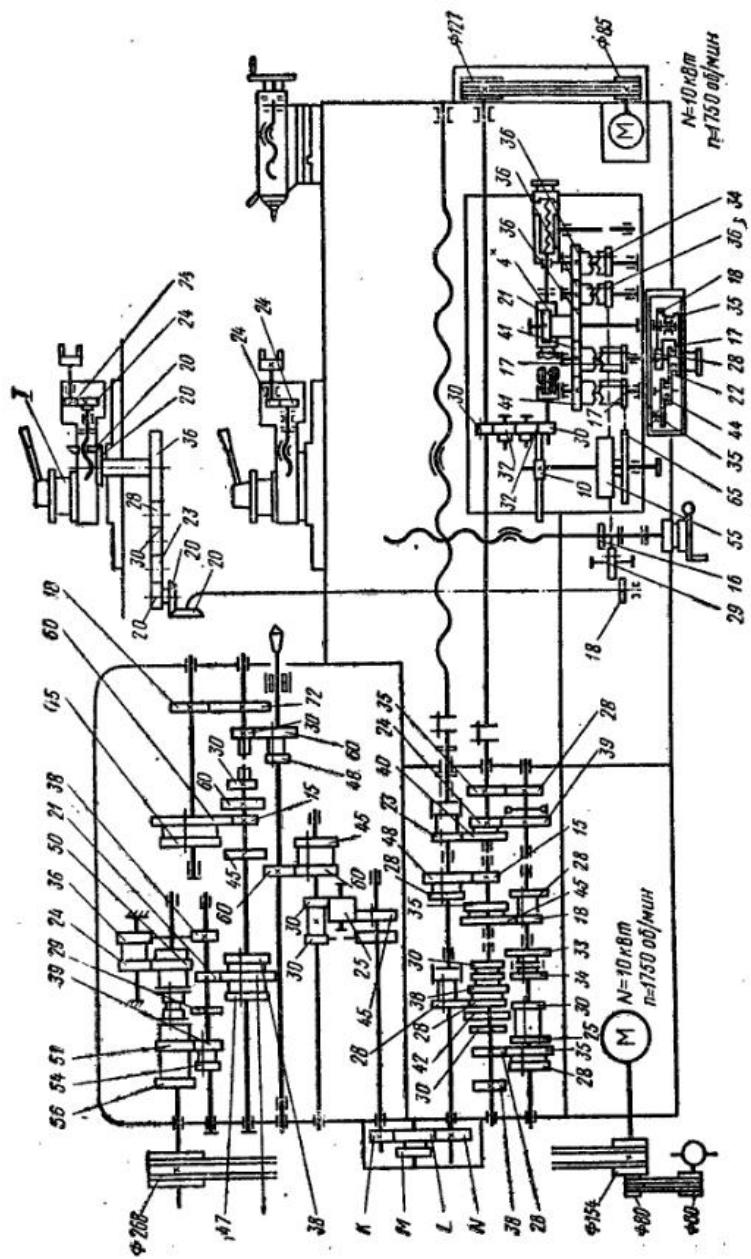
Кинематическая схема токарно-винторезного станка 16К20 (цифрами обозначены числа зубьев)
